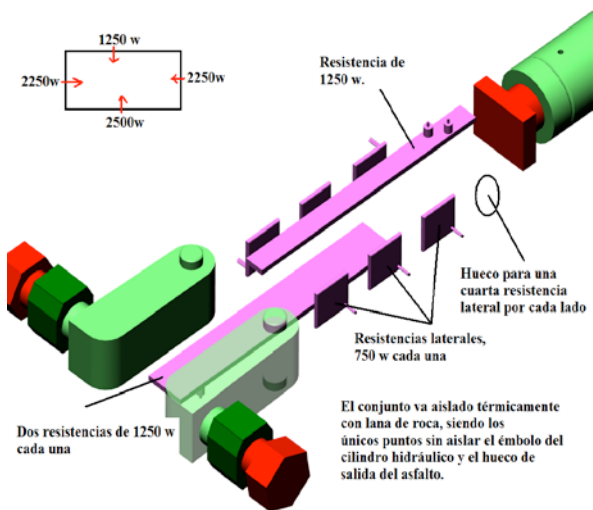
Dispositivo extrusor. Vista de los elementos de calefacción.
